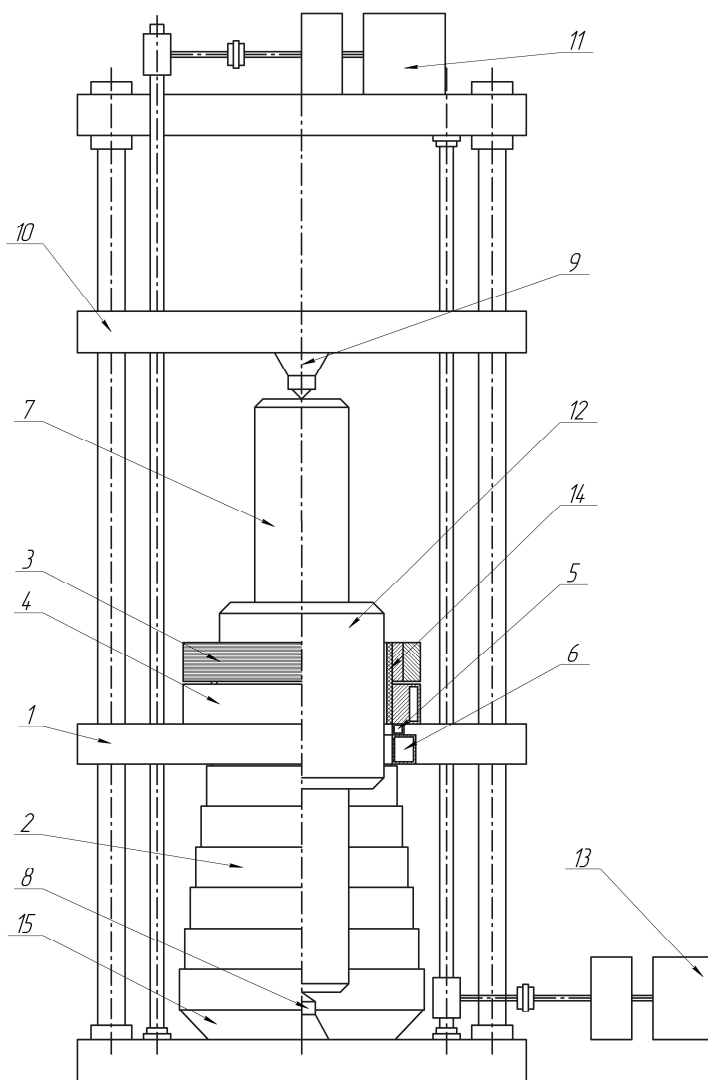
Установка индукционного нагрева с бегущим электромагнитным полем для закалки крупногабаритных валков прокатных станов
